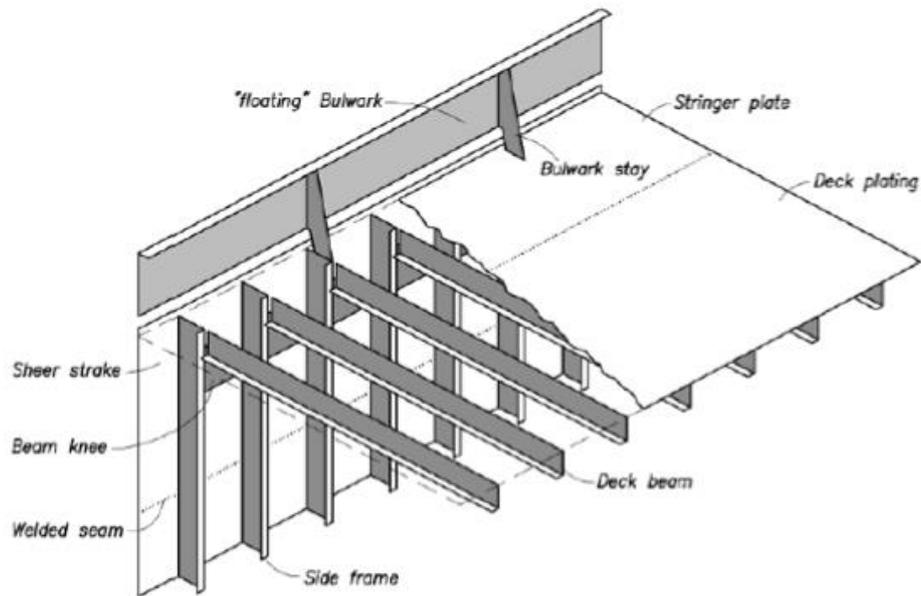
Estructura del puente con compuerta abierta – estructuras longitudinales
